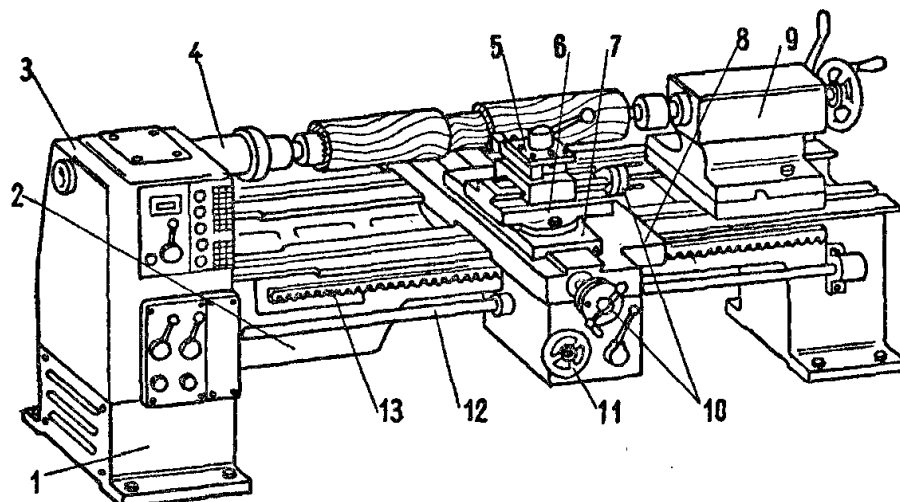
Токарний верстат з механічною подачею супорта і приставним лобовим пристроєм ТС-40:
